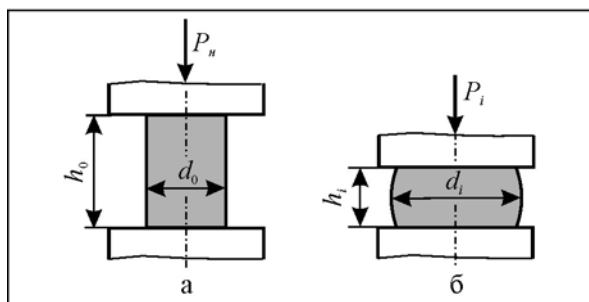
Схема відкритого осаджування суцільної заготовки: а – початкова фаза; б – проміжна фаза
